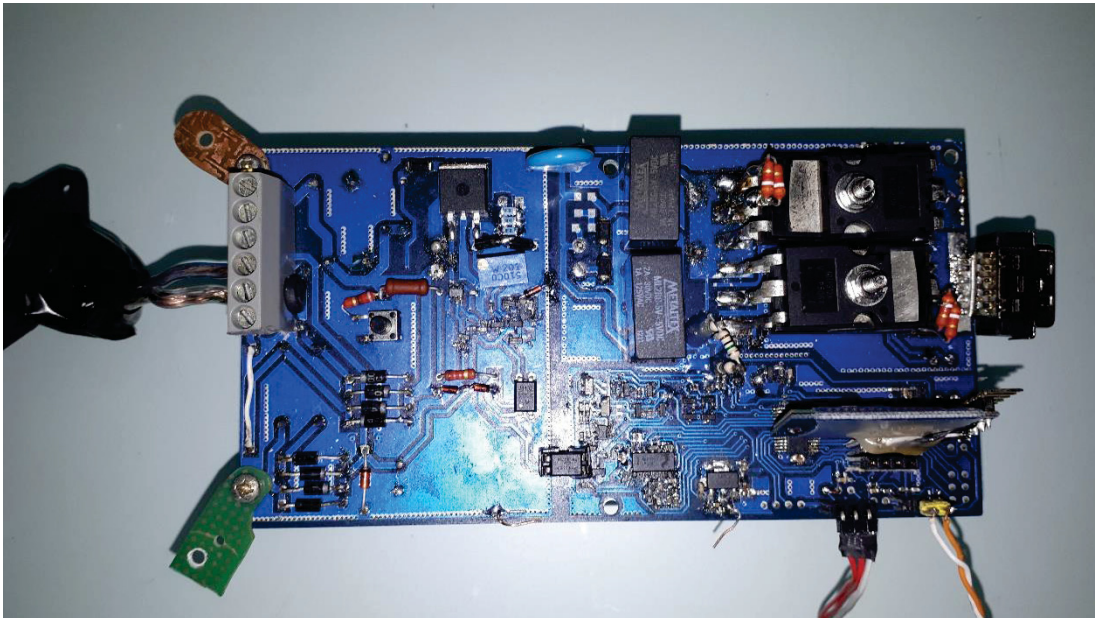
LAYOUT DA FACE INFERIOR DO SEGUNDO PROTÓTIPO
